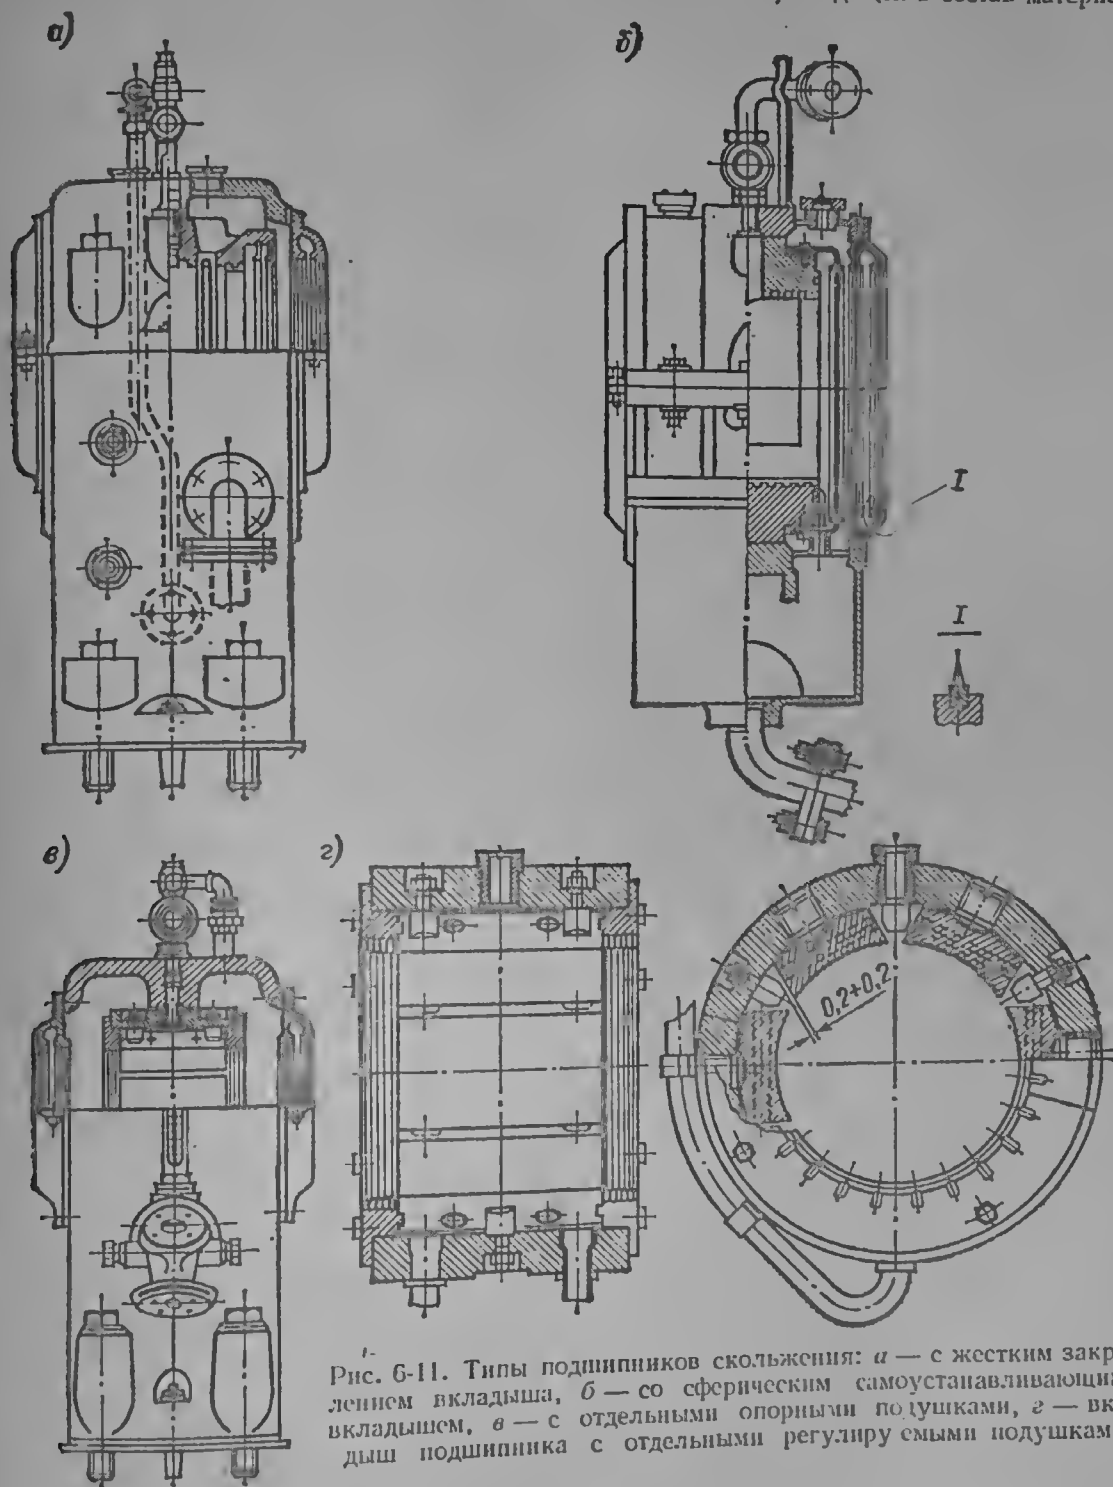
Типы подшипников скольжения: а — с жестким креплением вкладыша, б — со сферическим самоустанавливающимся вкладышем, в — с отдельными опорными подушками, г — вкладыш подшипника с отдельными регулирующими подушками
